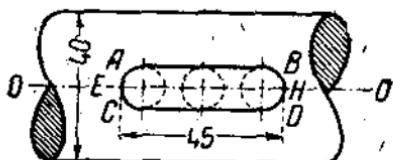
Изготовление шпоночного паза на валу для врезной призматической шпонки со скругленными торцами.
